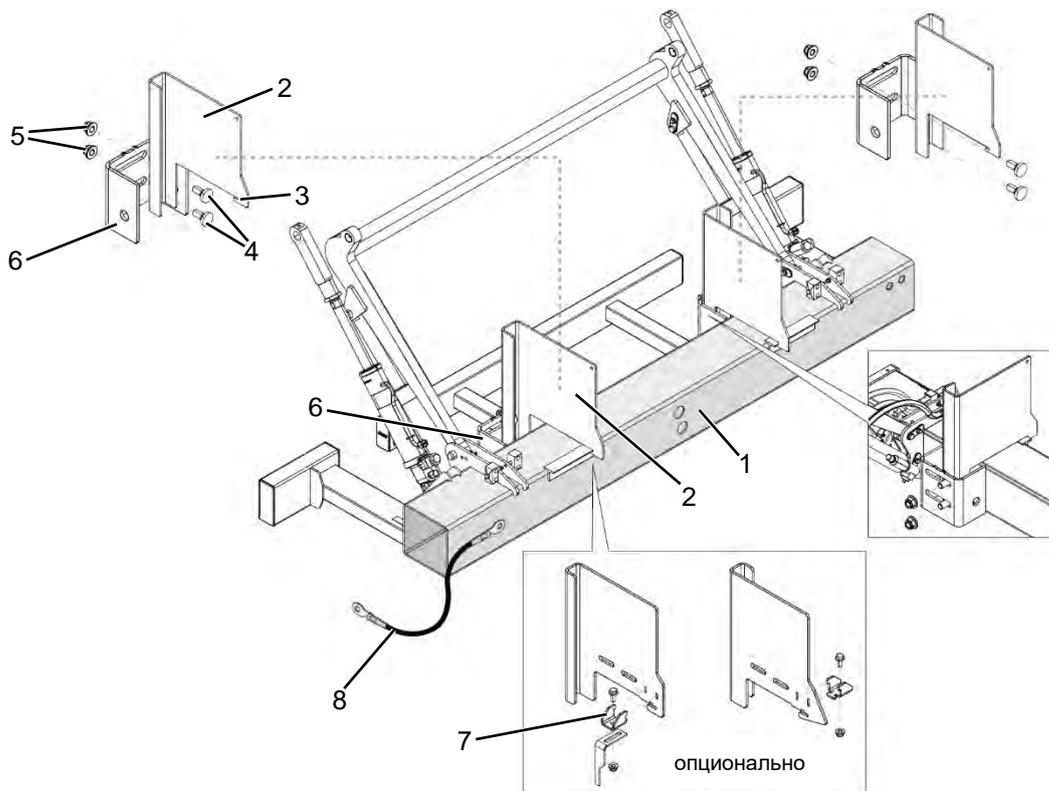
Предварительный монтаж с регулируемой высотой консолями с резьбовыми соединениями
